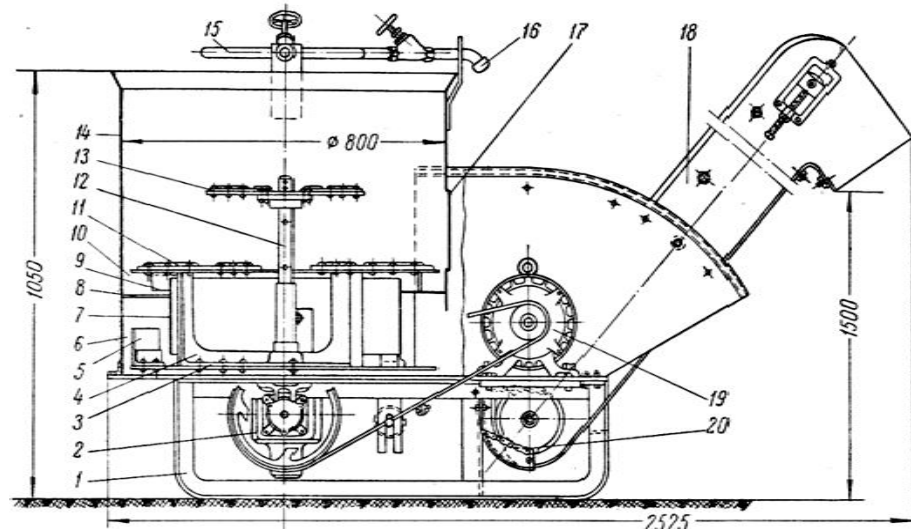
Схема дискової коренемийки-коренерізки: 1 - рама; 2 - кожух шестерень; 3 - нижній викидаючий диск; 4 - крилач; 5 - лопать нижнього диска; 6 - кільцева камера збору різаного продукту; 7 - внутрішній циліндр з ножами; 8 - кільцеве днище робочого циліндра; 9 - скребок нижнього мийного диска; 10 - грязьова кільцева камера; 11 - нижній мийний диск з отворами; 12 - вал; 13 - верхній мийний диск; 14 - корпус робочого циліндра; 15 - кільцевий трубопровід; 16 - патрубок; 17 - засувка верхнього випускного люка; 18- ланцюговий-скребковий транспортер; 19 - електродвигун; 20 - приводний ланцюг транспортера
